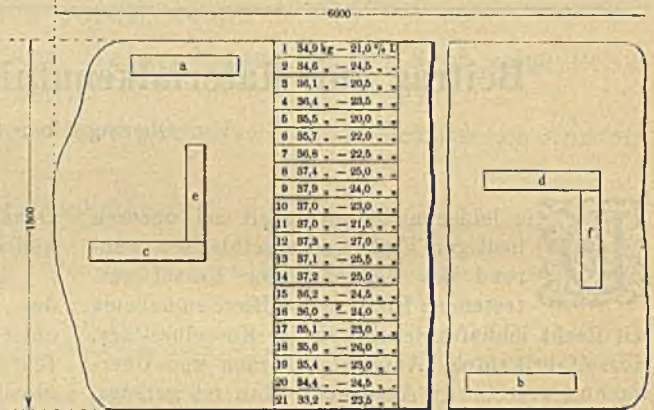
Schweißisenblech, 15 mm dick.
